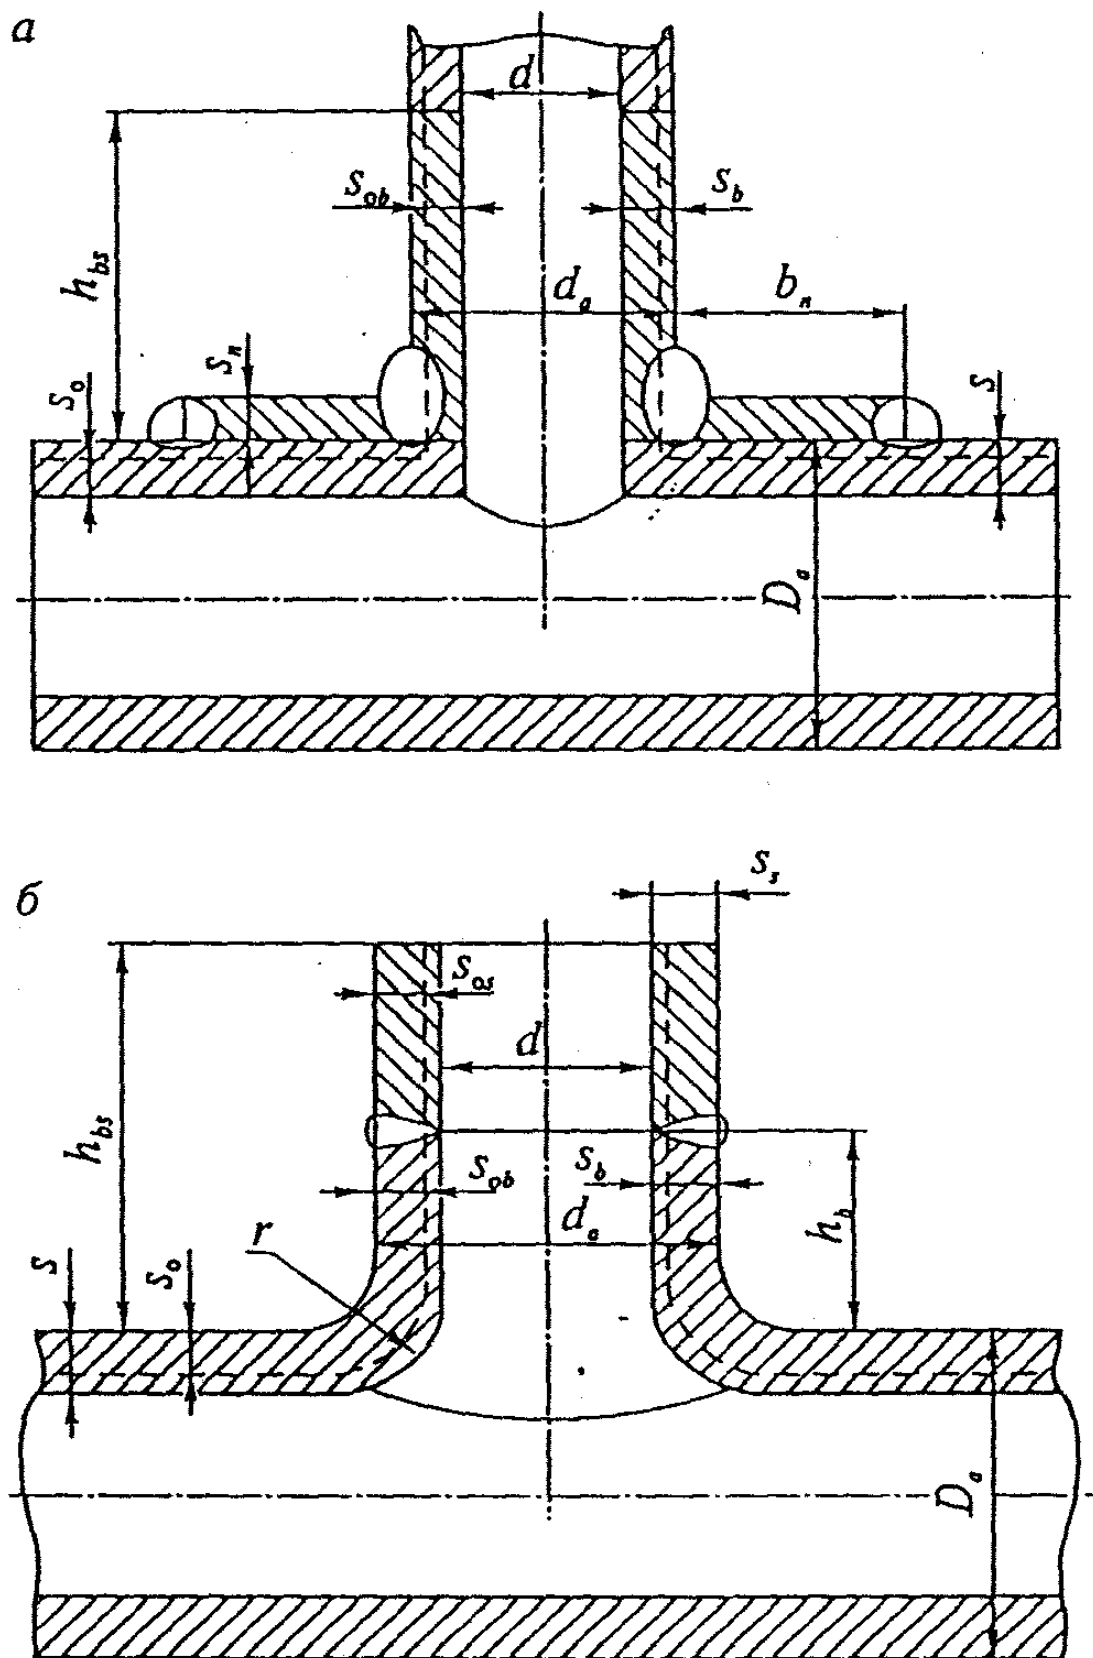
Тройник: *a* — сварной; *б* — штампованный
